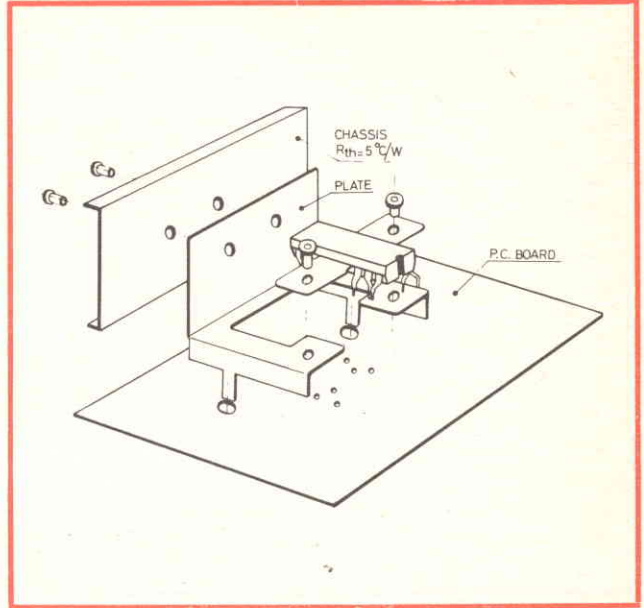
Esempio di montaggio nel quale il telaio può essere montato a parte.
